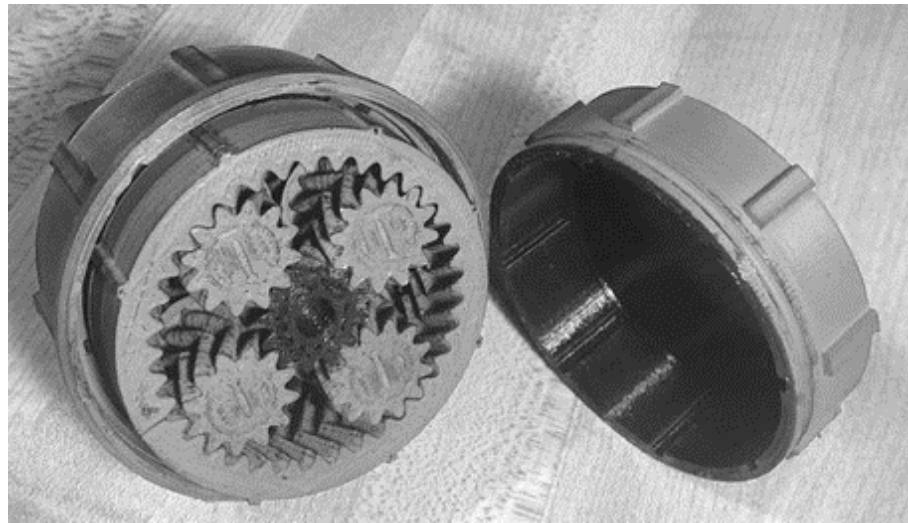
Внутрішня конструкція планетарного редуктора нижнього суглоба
